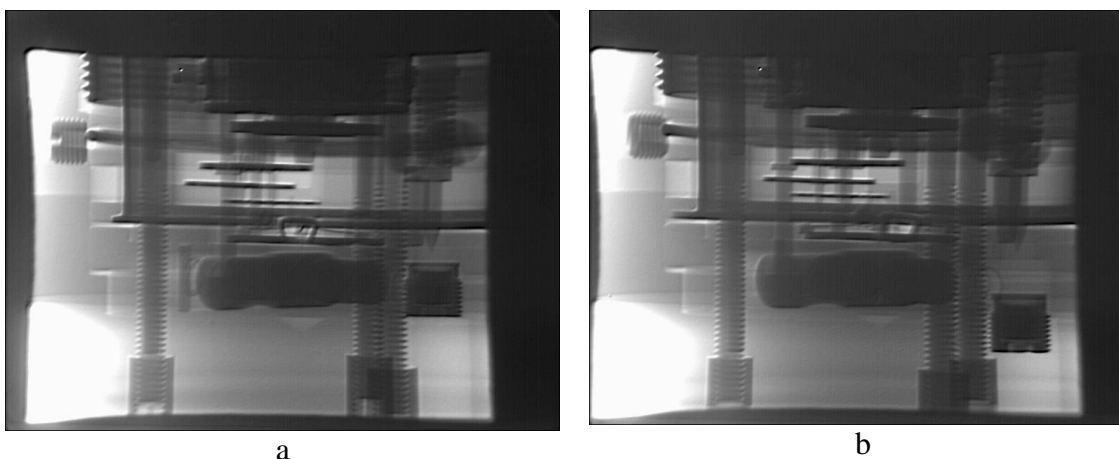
Korozja spłonek zapalających zapalnika DC-1 z NGP-76
